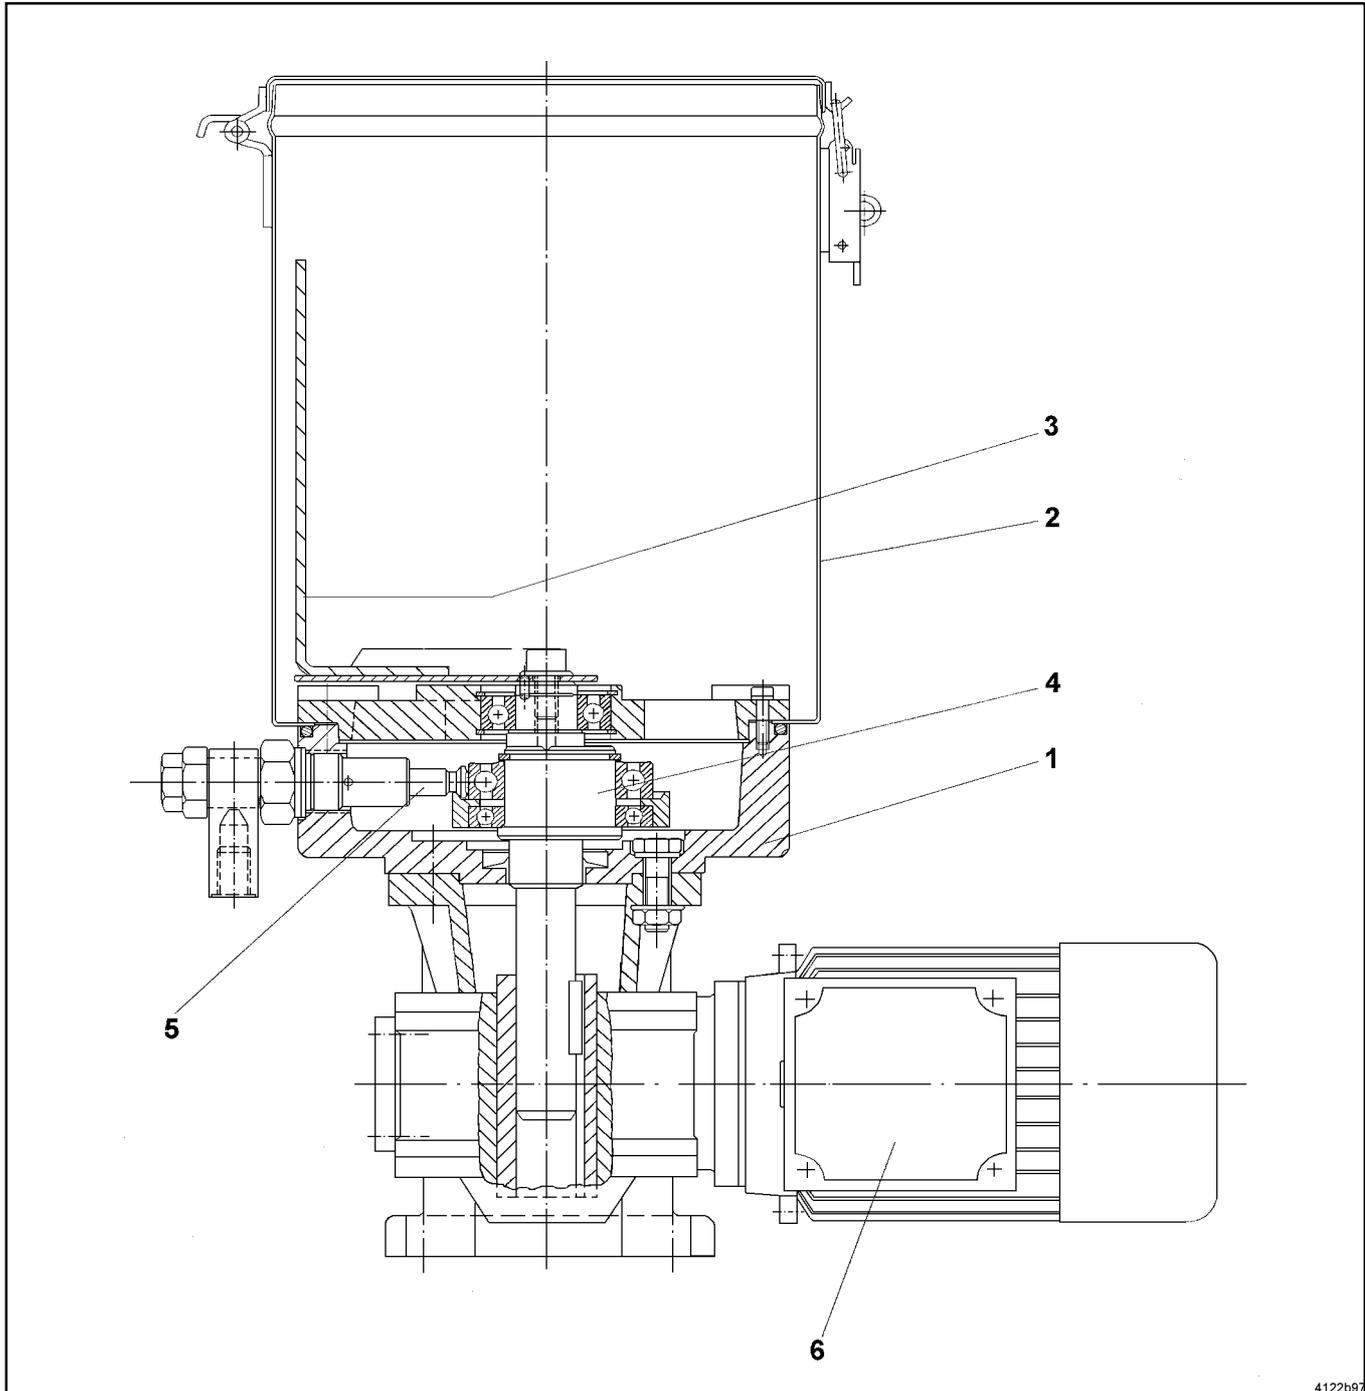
Schnittzeichnung der Pumpe ZPU 01/02
